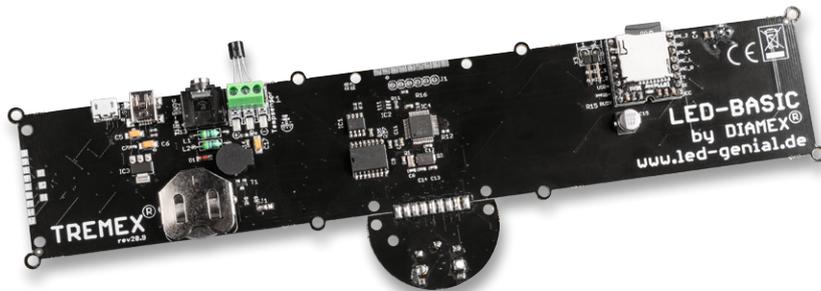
Die Elektronik des Uhrenbausatzes kommt komplett bestückt ins Haus.
